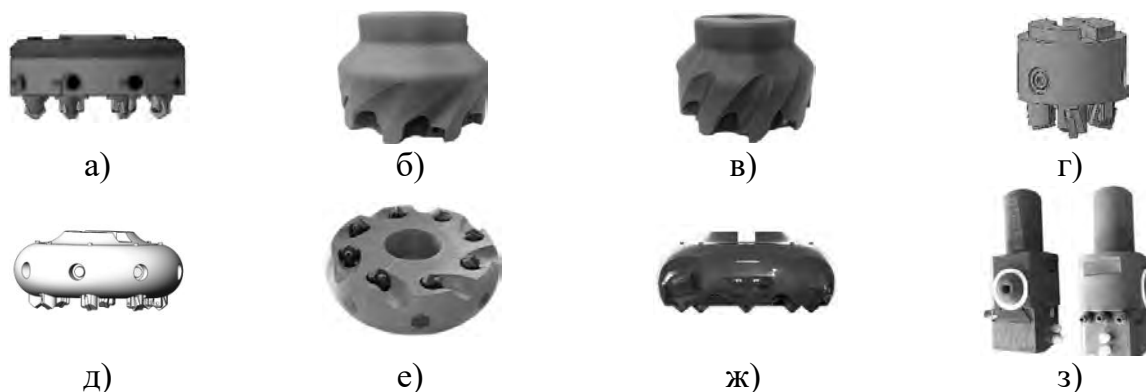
Макеты сборных торцевых фрез в форме диска (а), диска и конуса (б и в), цилиндра (г), тора (д-ж) и расточной головки в форме цилиндра (з)
